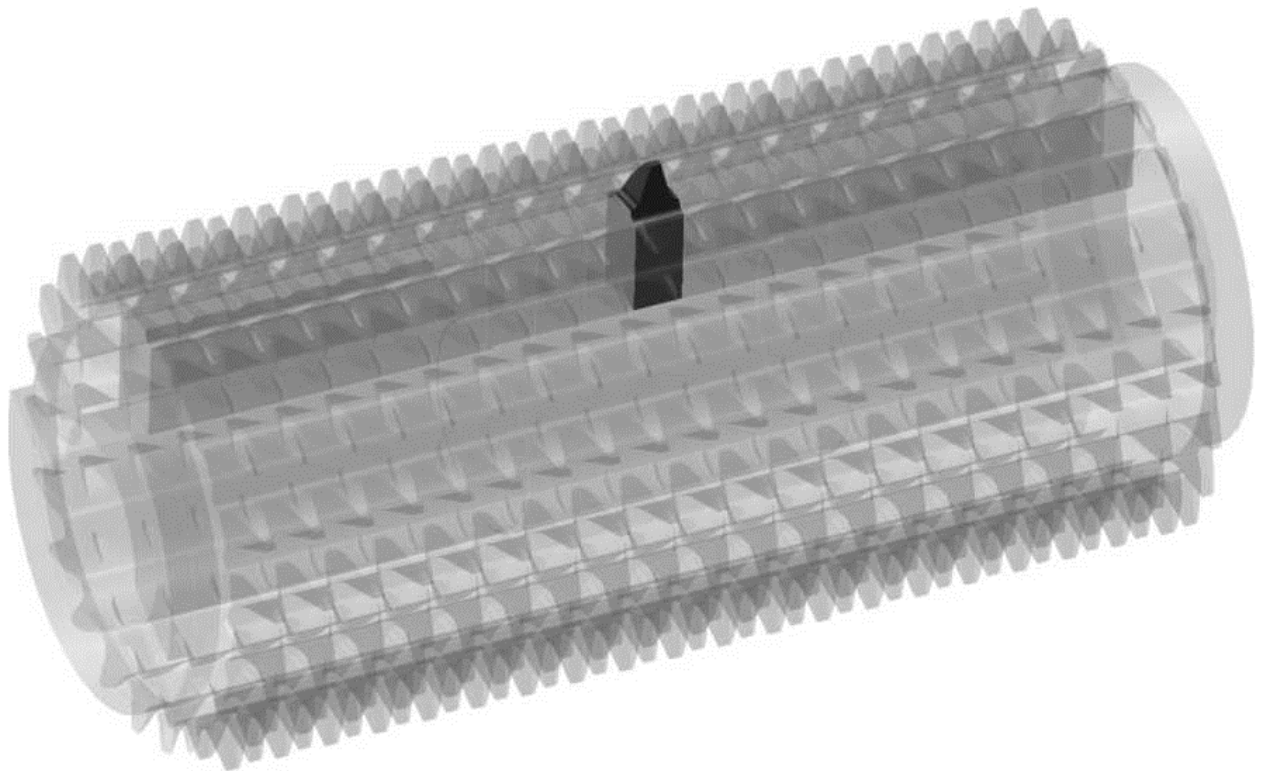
Розташування робочого зуба на черв'ячній фрезі
